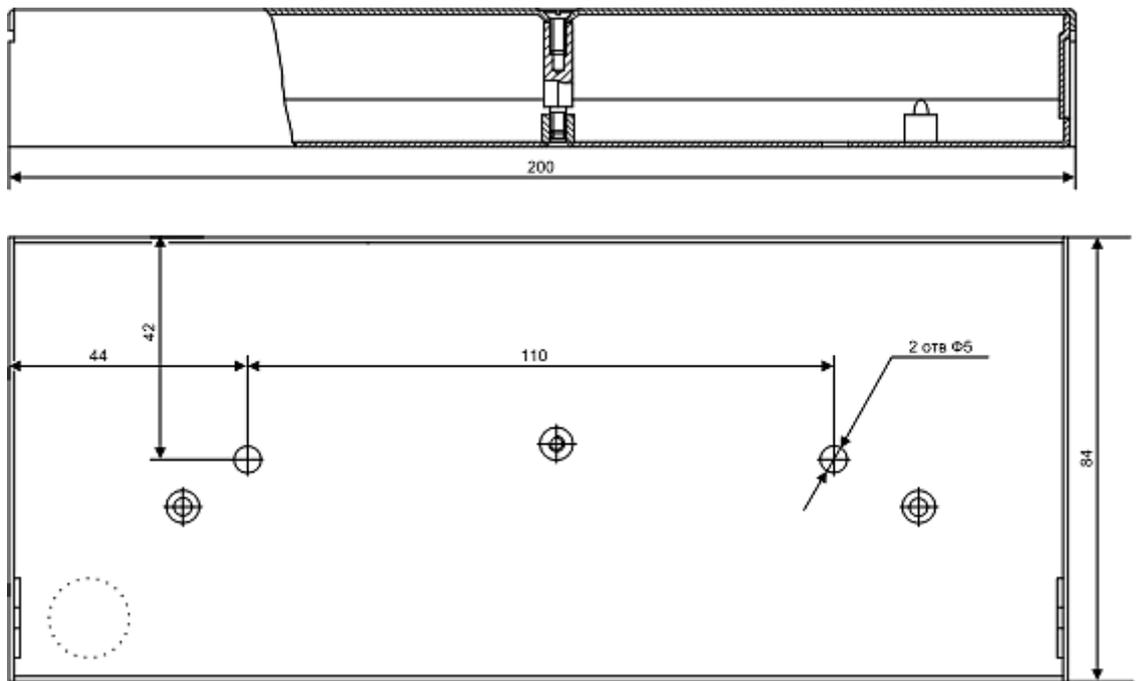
Конструкция и размеры корпуса КСП-А4/8 и ИСА-8
